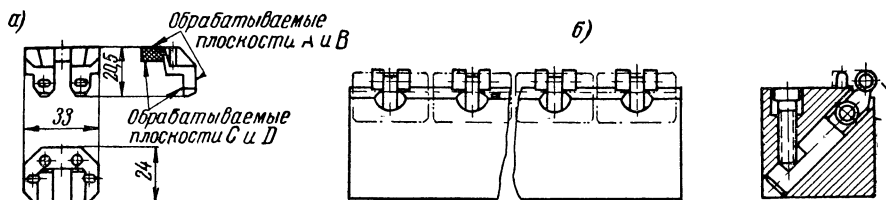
Эскиз обрабатываемой детали (а) и приспособления для плоского шлифования (б).
